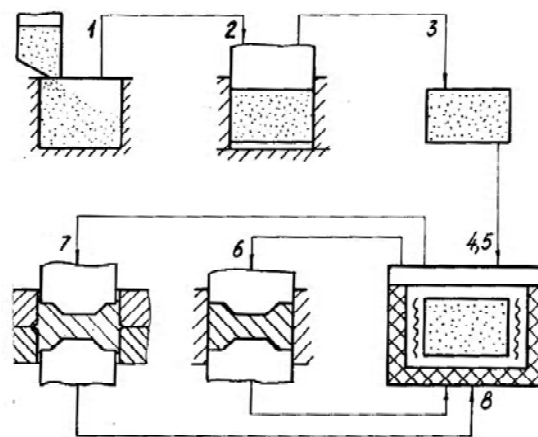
Технологічна схема виробництва конструкційних виробів при гарячому штампуванні порошкових заготовок: 1 – засипка порошку в прес-форму; 2 – холодне пресування заготовки; 3 – витягання заготовки; 4, 5 – співання і нагрівання заготовки; 6, 7 – відповідно штампування в закритому штампі та з елементами витікання; 8 – термічна обробка
